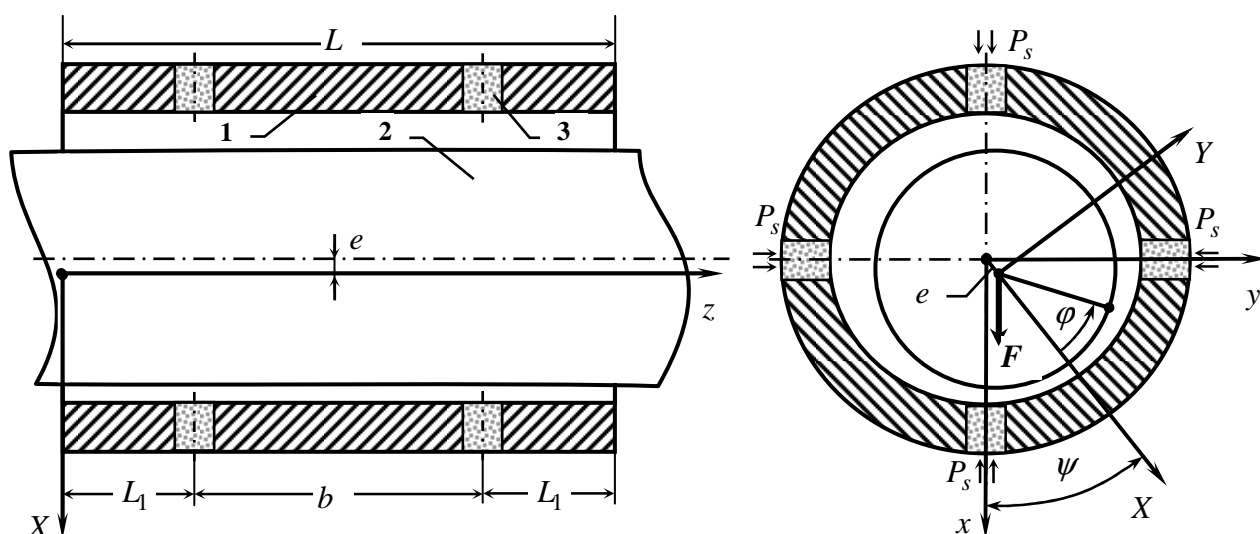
Газостатический подшипник с двумя рядами пористых вставок:
